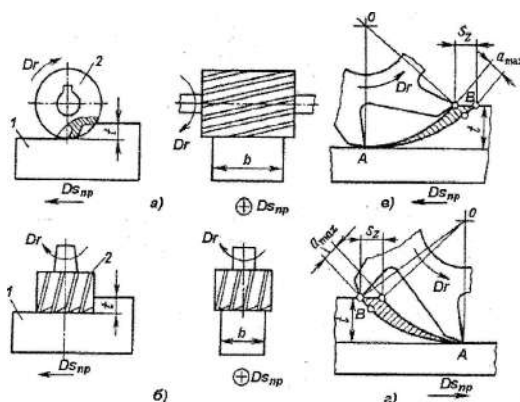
Схемы фрезерования торцовой и цилиндрической фрезами
